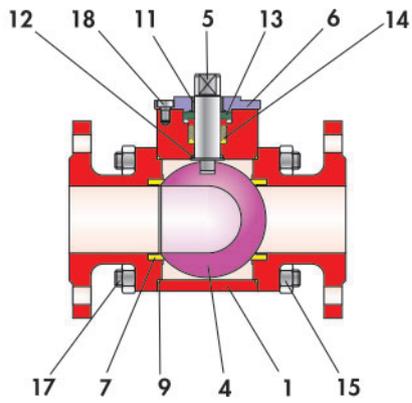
BR 26l, horizontaler 3-Wege Kugelhahn mit L-Bohrung
